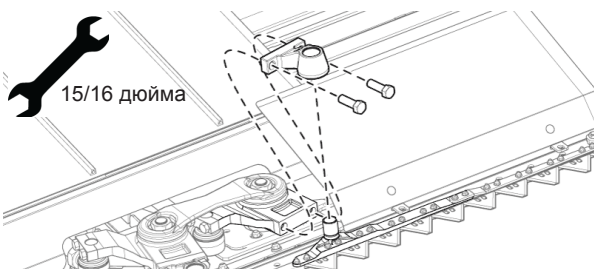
Снятие корпуса подшипников с головки левого ножа.
